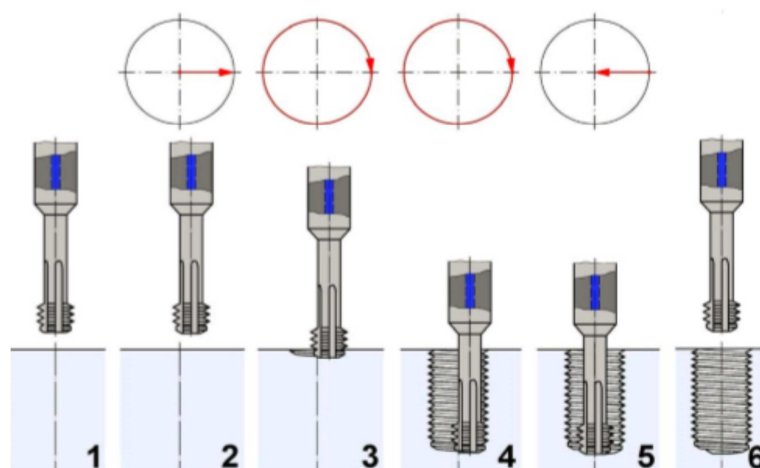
Hřebenová válcová nástrčná fréza [6].
